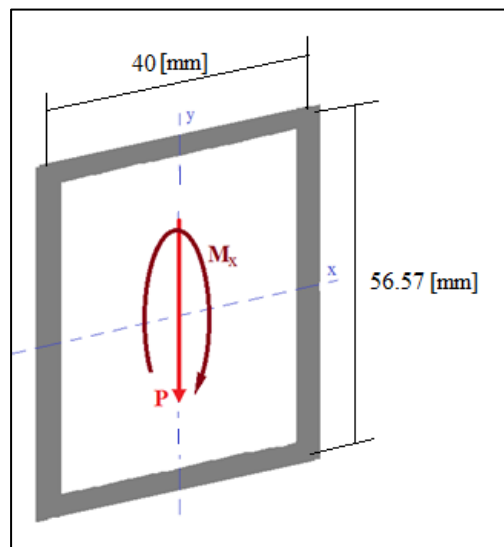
Fuerzas y momentos en la unión soldada.
